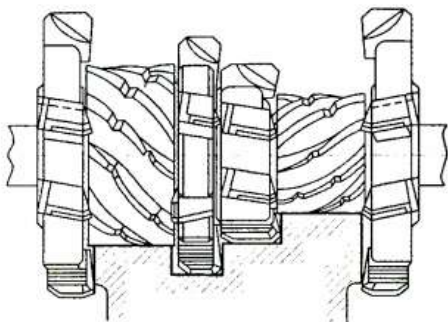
Набір фрез для оброблення фасонної поверхні
